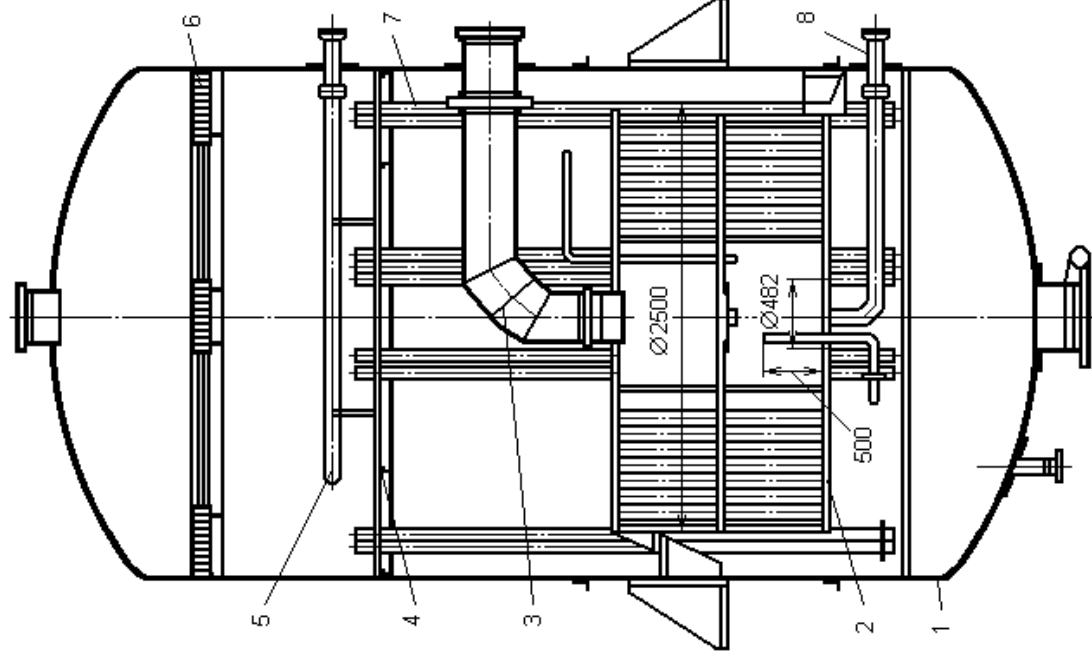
Общий вид испарителя поверхностного типа: 1 – корпус; 2 – греющая секция; 3 – подвод греющего пара; 4 – паропромывочный дырчатый лист; 5 – водораспределительное устройство; 6 – жалюзийный сепаратор; 7 – опускные трубы; 8 – отвод конденсата греющего пара
